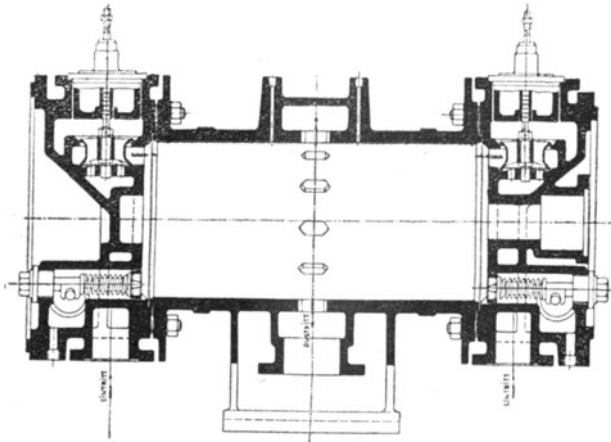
Gleichstromzylinder der Cottbusser Maschinenfabrik A.-G. mit Zuschaltventilen für Auspuffbetrieb.
